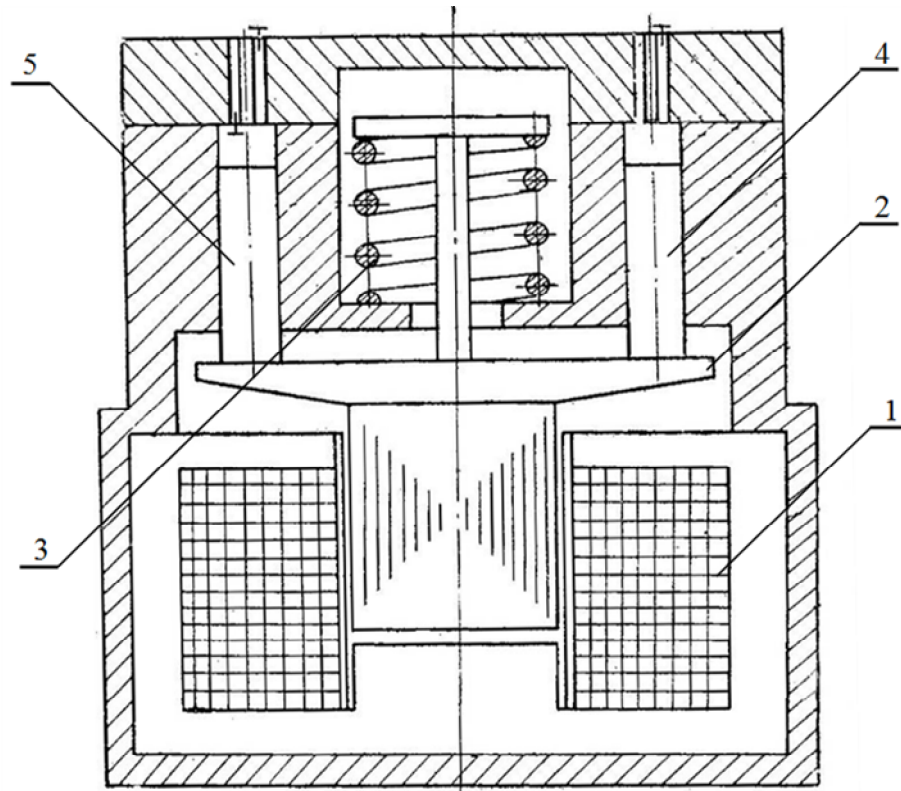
Электромагнитный однокатушечный поршневой компрессор
